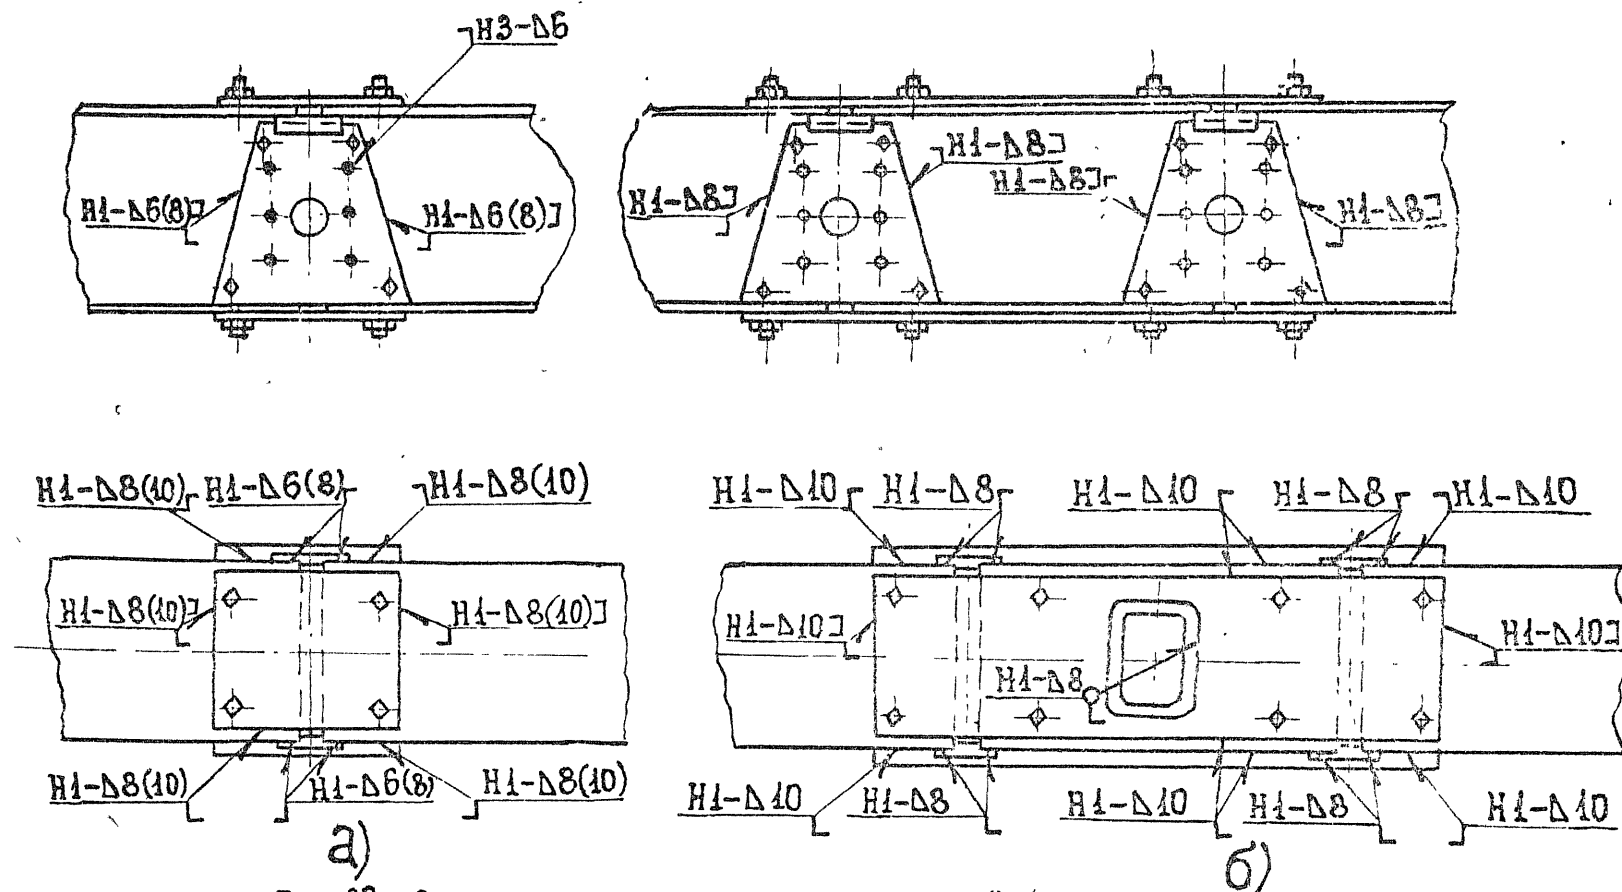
Окончательная сварка стыка концевой балки.
